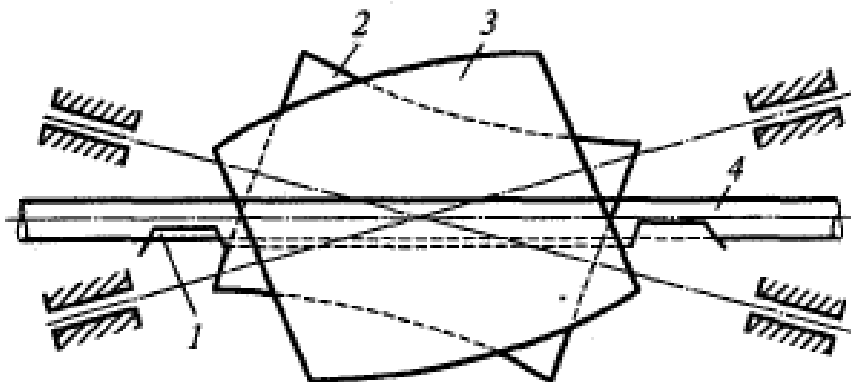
Схема правки на правильно-калібрувальному верстаті: 1 – призматичні напрямні; 2, 3 – ролики; 4 – пруток
